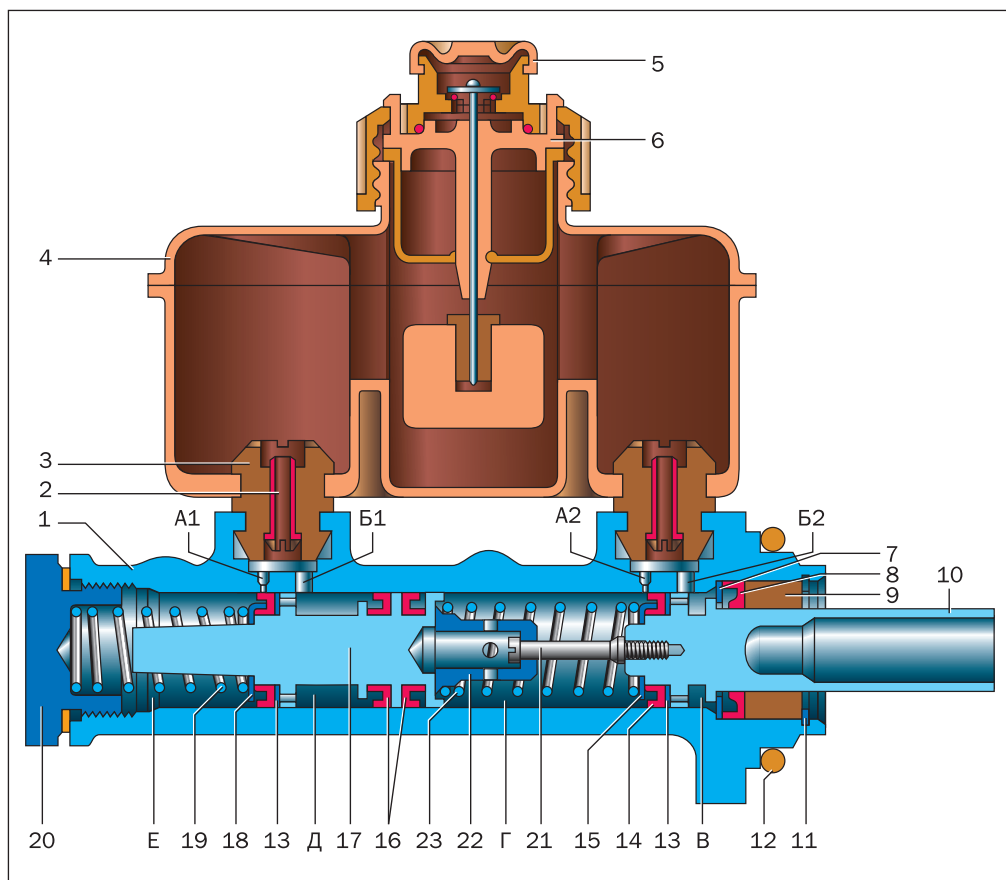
Главный тормозной цилиндр типа тандем: А1, А2 — компенсационные отверстия; Б1, Б2 — перепускные отверстия; В, Г, Д, Е — полости; 1 — корпус; 2 — трубка; 3 — соединительная втулка; 4 — бачок; 5 — защитный колпачок; 6 — датчик сигнализатора аварийного падения уровня тормозной жидкости; 7 — упорное кольцо; 8 — наружная манжета; 9 — направляющая втулка; 10, 17 — поршни; 11 — стопорное кольцо; 12 — уплотнительное кольцо; 13 — шайба поршня; 14, 16 — манжеты; 15, 18 — упорные шайбы; 19 — пружина; 20 — пробка; 21 — болт держателя пружины; 22 — держатель пружины; 23 — пружина
